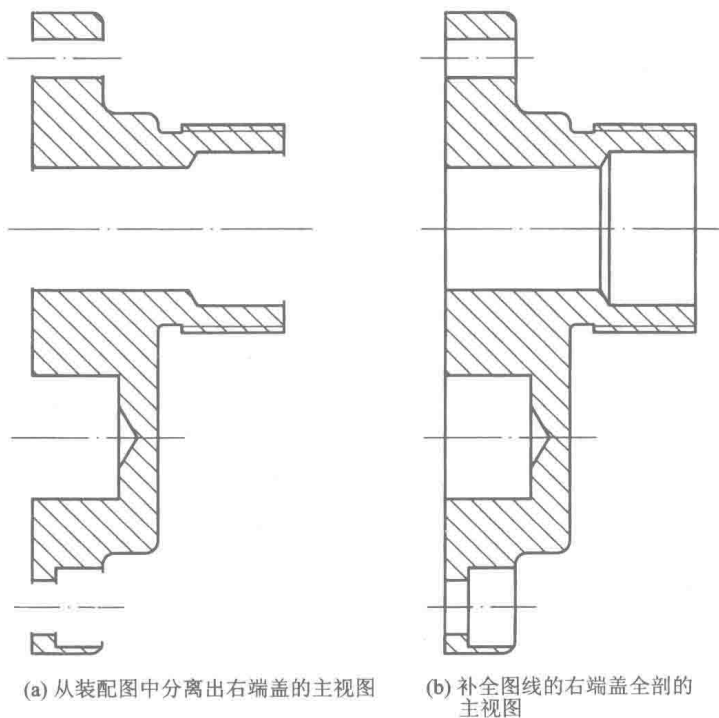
由齿轮油泵装配图拆画右端盖零件图
